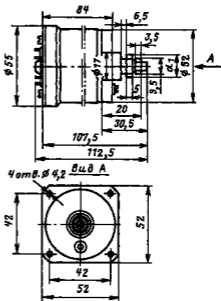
Габаритные и установочные размеры двигателя ЭМ-221. Значения размера  $d_1$  приведены ниже.
